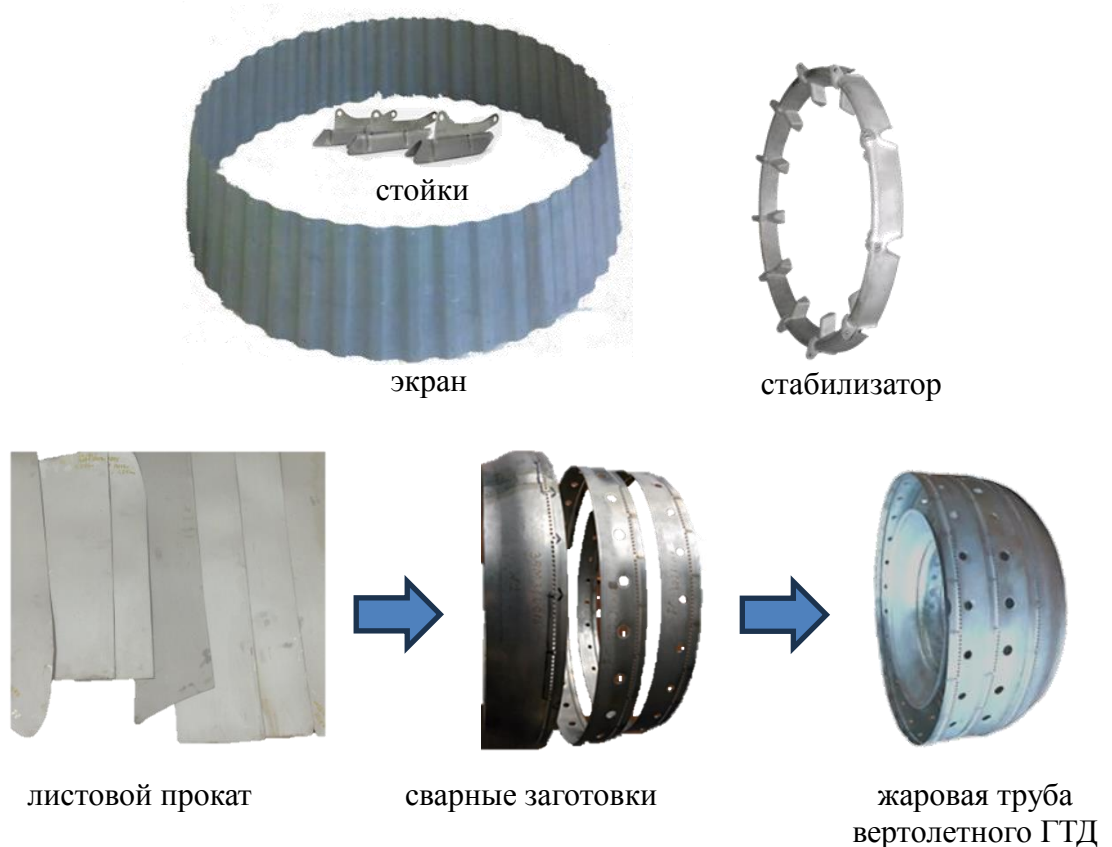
Детали и узлы, изготовленные из сплава ВЖ171
